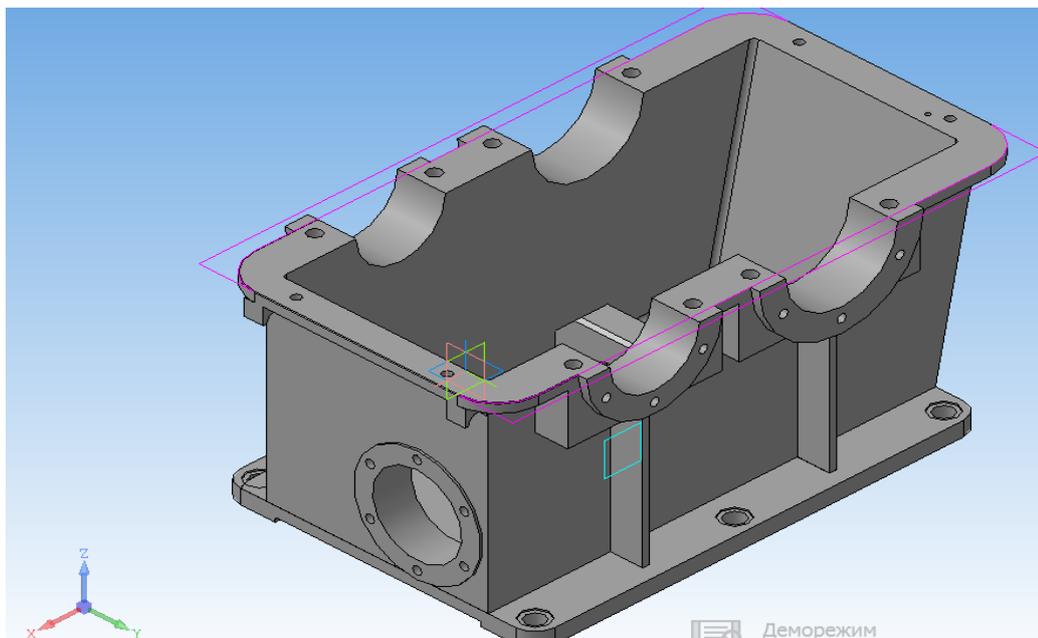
Объемная модель детали «Корпус редуктора»
